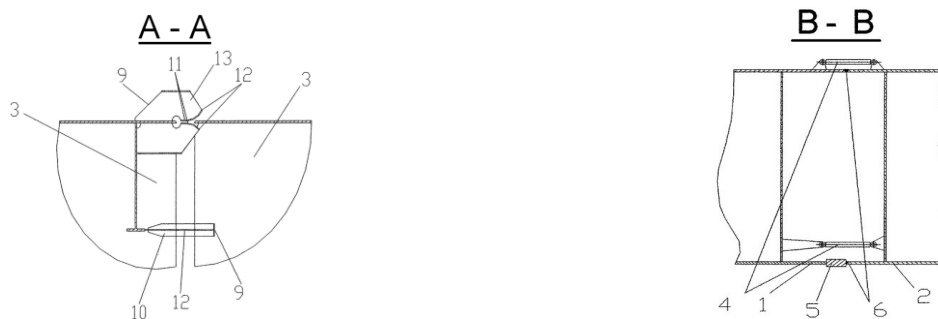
Схема сборки крупных блоков судового корпуса на плаву:
